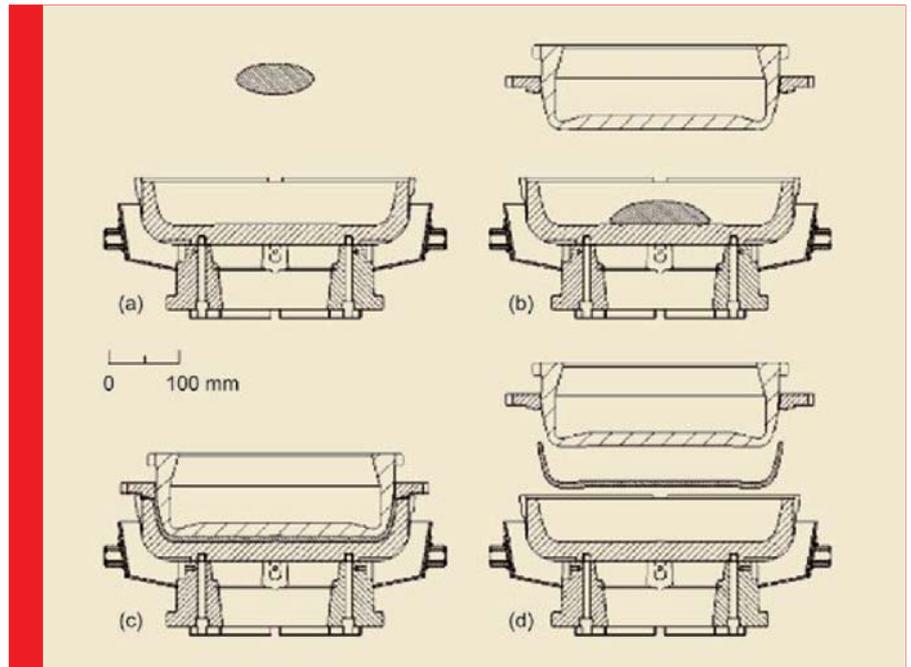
Principais etapas do processo de moldagem do vidro por prensagem^[3]: a) abastecimento do vidro; b) prensagem; c) manutenção da pressão; d) desmoldagem.
